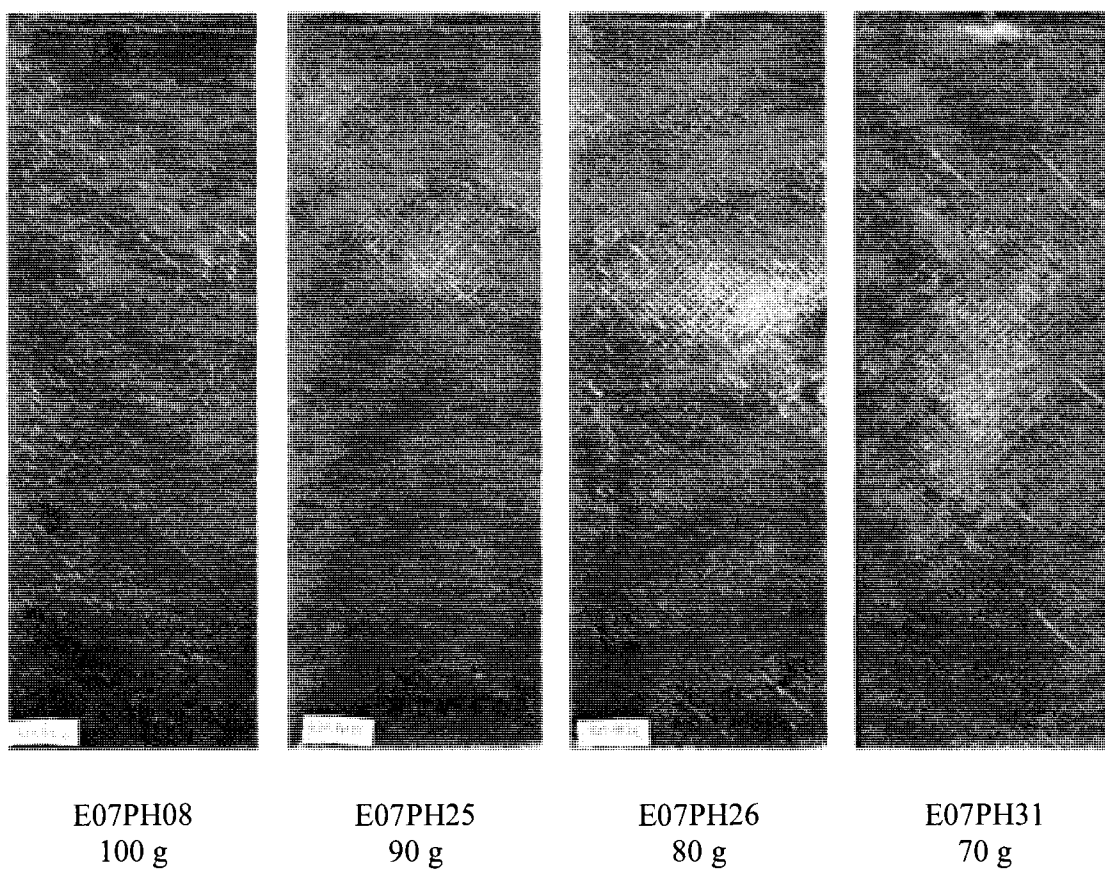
Pièces finales vues du côté moule pour différente quantité de résine.
